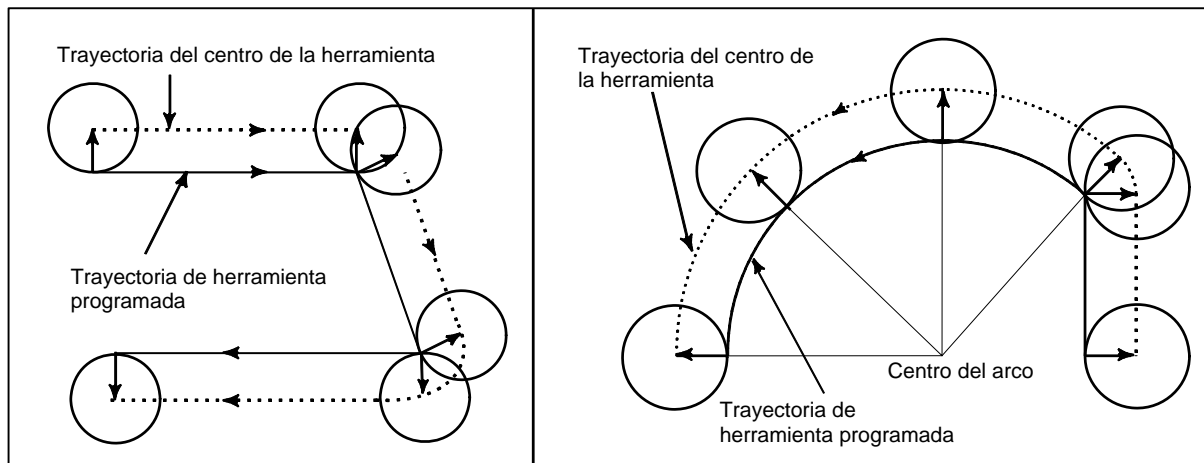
(b) Control en la dirección perpendicular, izquierda (G41.1)
